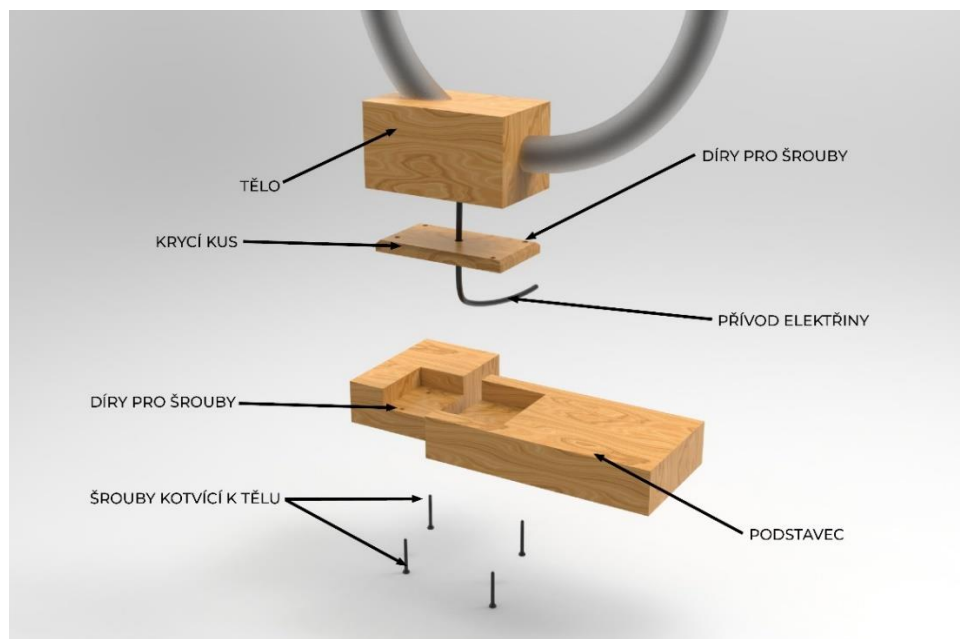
Vnitřní mechanismy a komponenty těla
